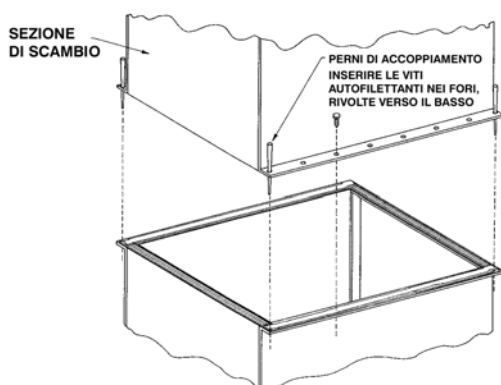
Accoppiamento della sezione ventilante alla sezione bacino.
